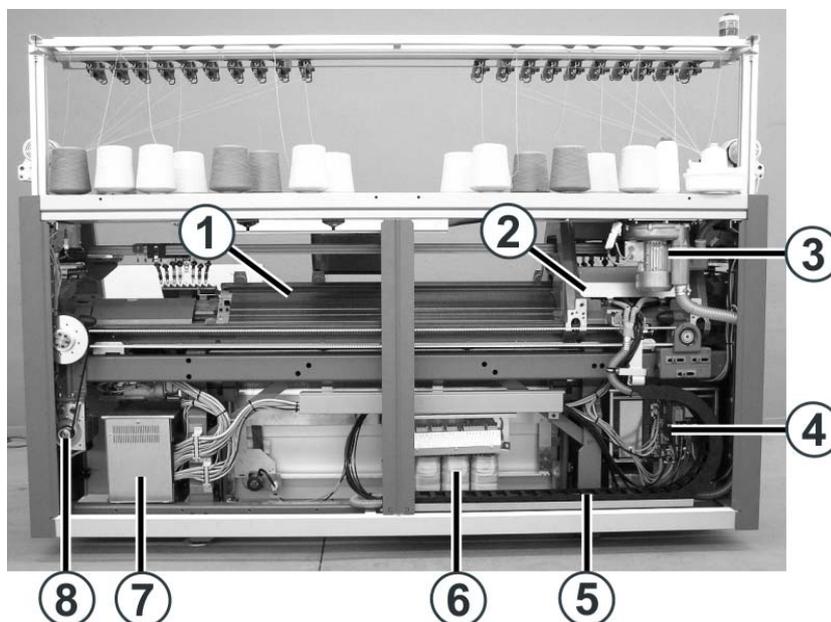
Face arrière (sans segments de paroi arrière)
